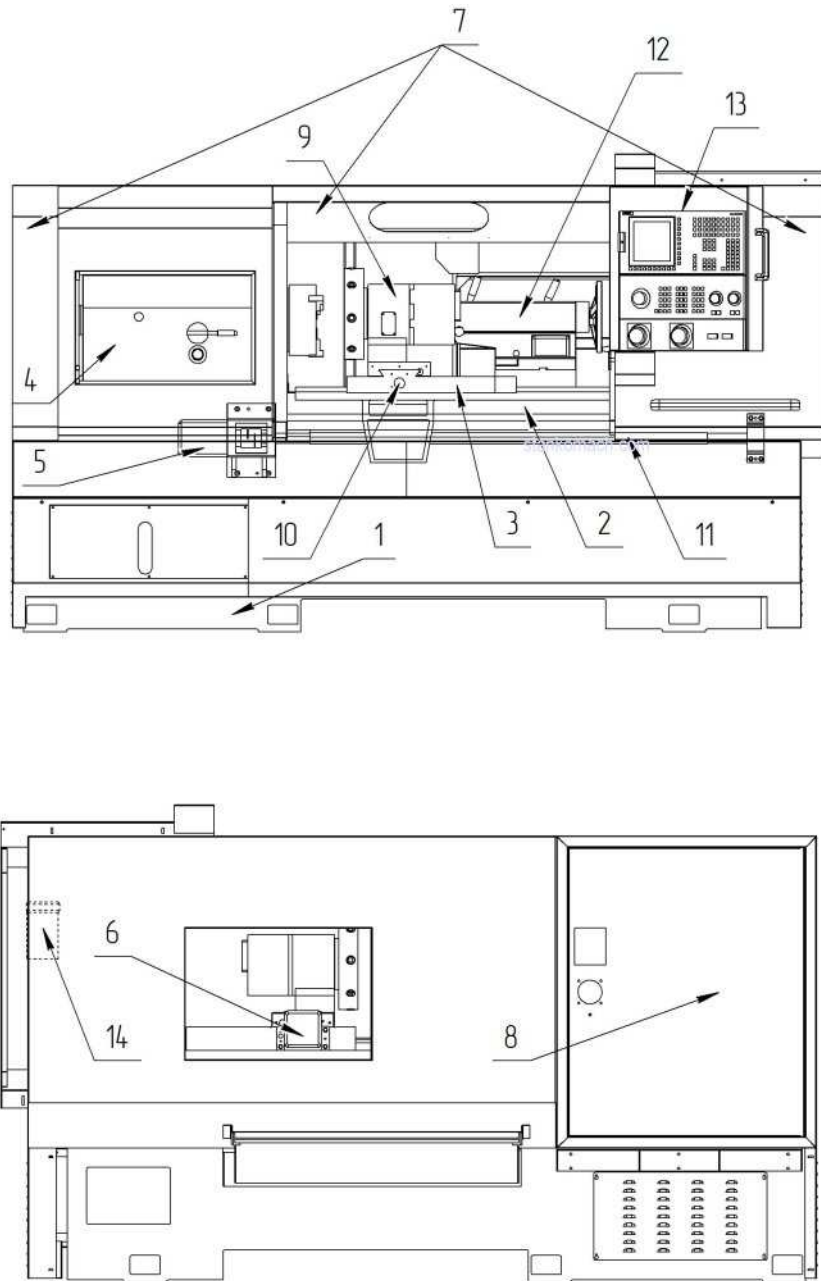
Основні вузли: 1- база; 2- станина; 3 – суппорт; 4 – бабка шпindelьна; 5 – привод повздовжнього переміщення; 6 – привод поперечного переміщення; 7 – огороження нерухомі та рухомі елементи; 8 – шкаф електроапаратури; 9 – револьверна головка; 10 – гвинтова кульова пара поперечного переміщення; 11 - гвинтова кульова пара повздовжнього переміщення; 12 – бабка задня; 13 – пульт управління з системою ЧПУ; 14 – система централізованого імпульсивного змащування
